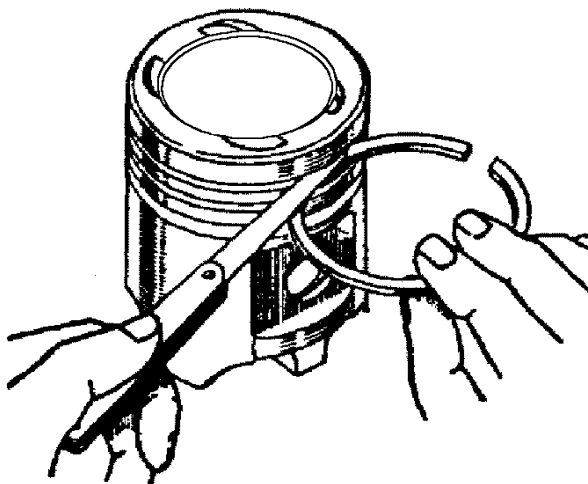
Проверка бокового зазора между поршневым кольцом и канавкой в поршне
